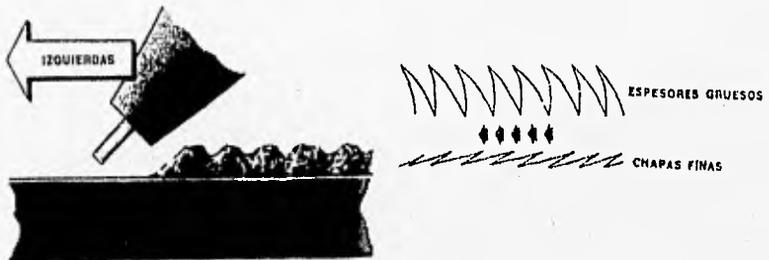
MOVIMIENTOS DE LA PISTOLA, PARA LA SOLDADURA MIG de los aceros inoxidable.
